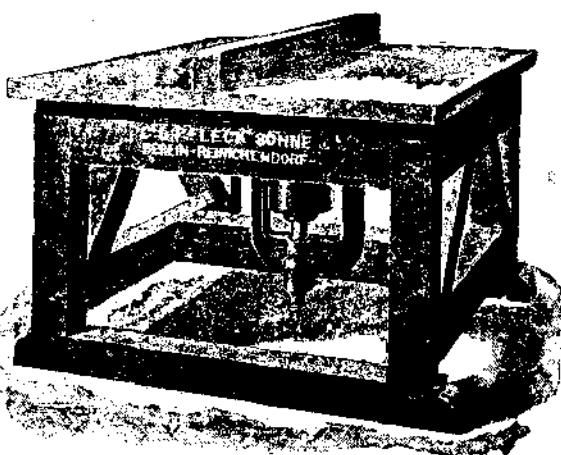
Горизонтальный песочно-бумажный шлифовальный станок.
